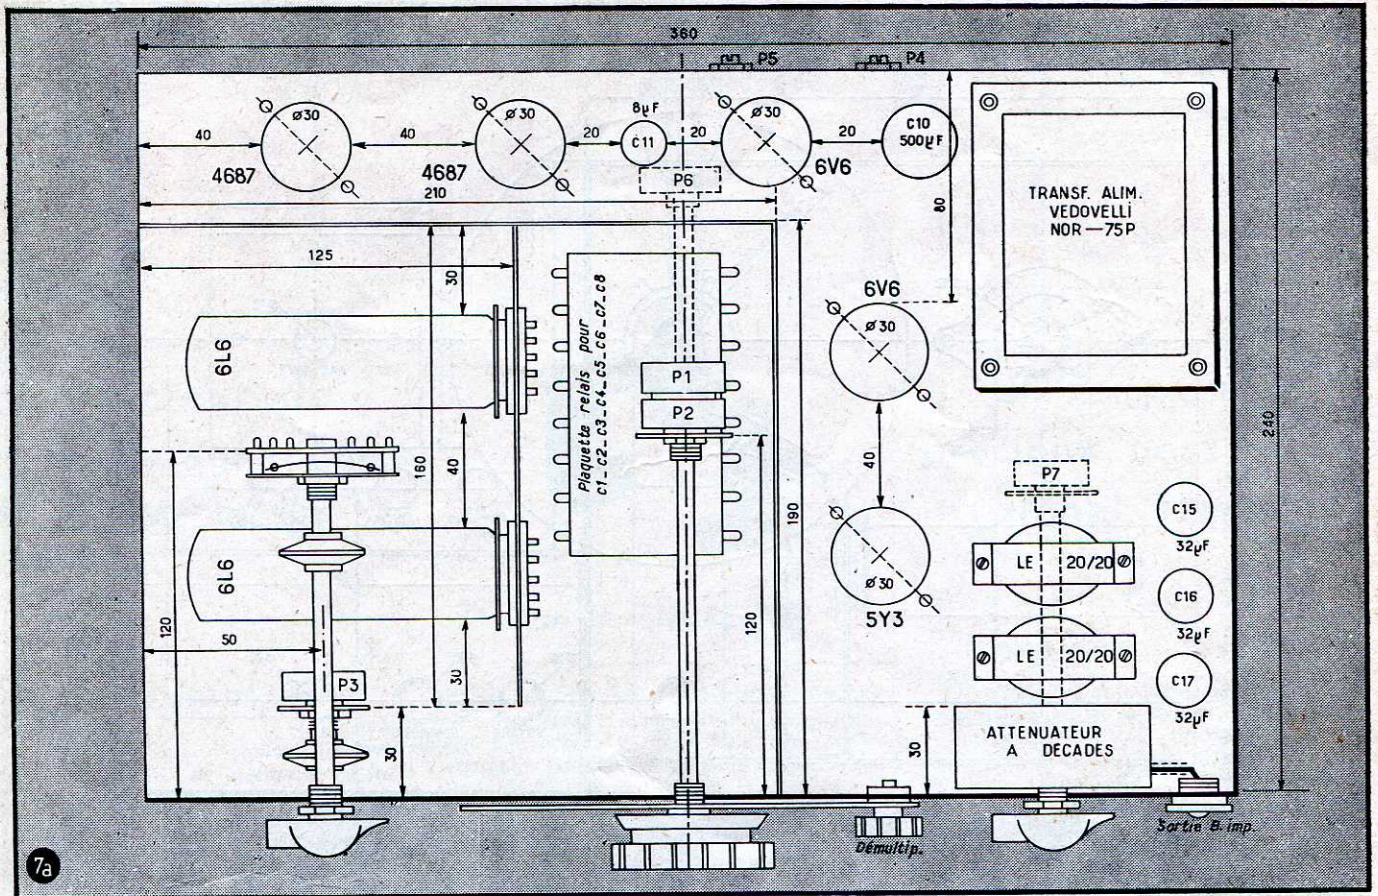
a. — Vue de dessus du générateur, blindages enlevés. La disposition des principales pièces a été indiquée.
